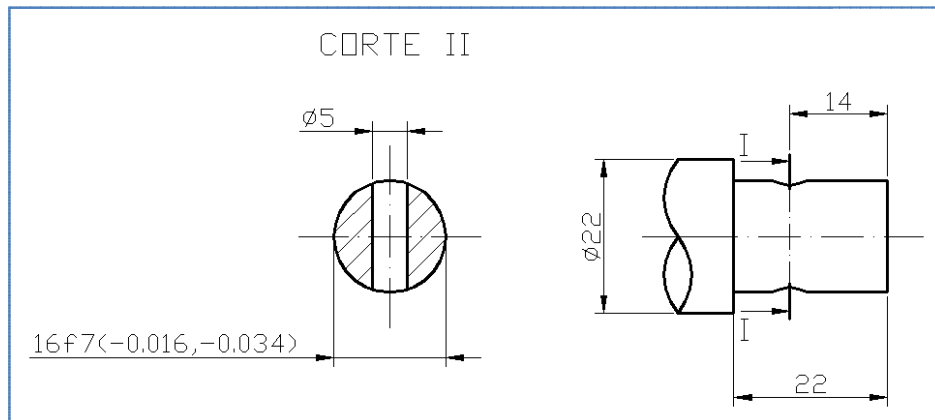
Diseño del extremo derecho del eje del subconjunto izquierdo
